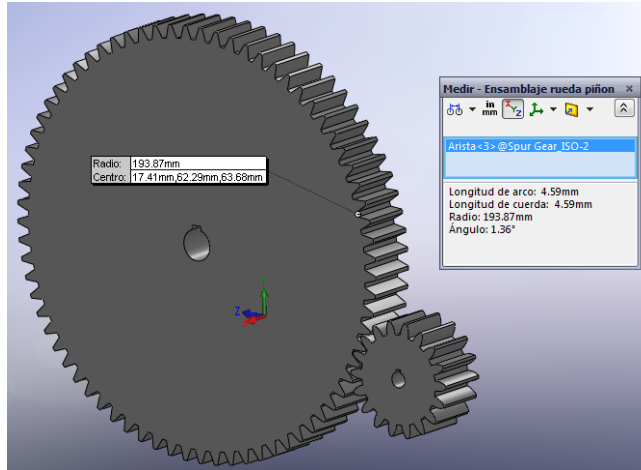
Dimensiones de la rueda A (volante principal)
